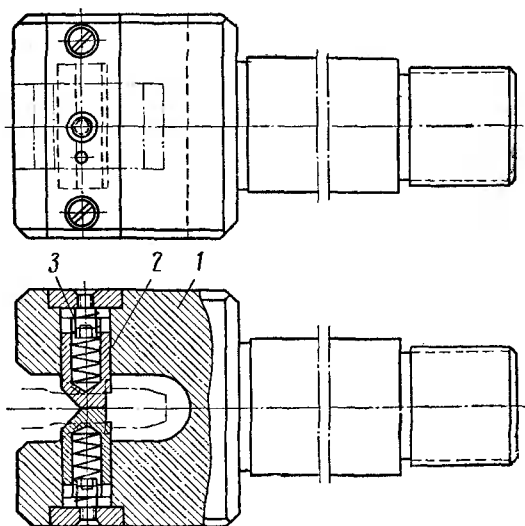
Быстросменный патрон для крепления протяжек типа шпоночных
